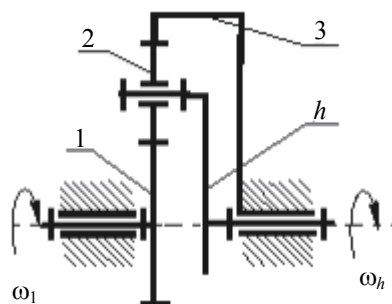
Кинематическая схема планетарного редуктора: 1 – шестерня; 2 – сателлит; 3 – эпицикл;  $h$  – водило
